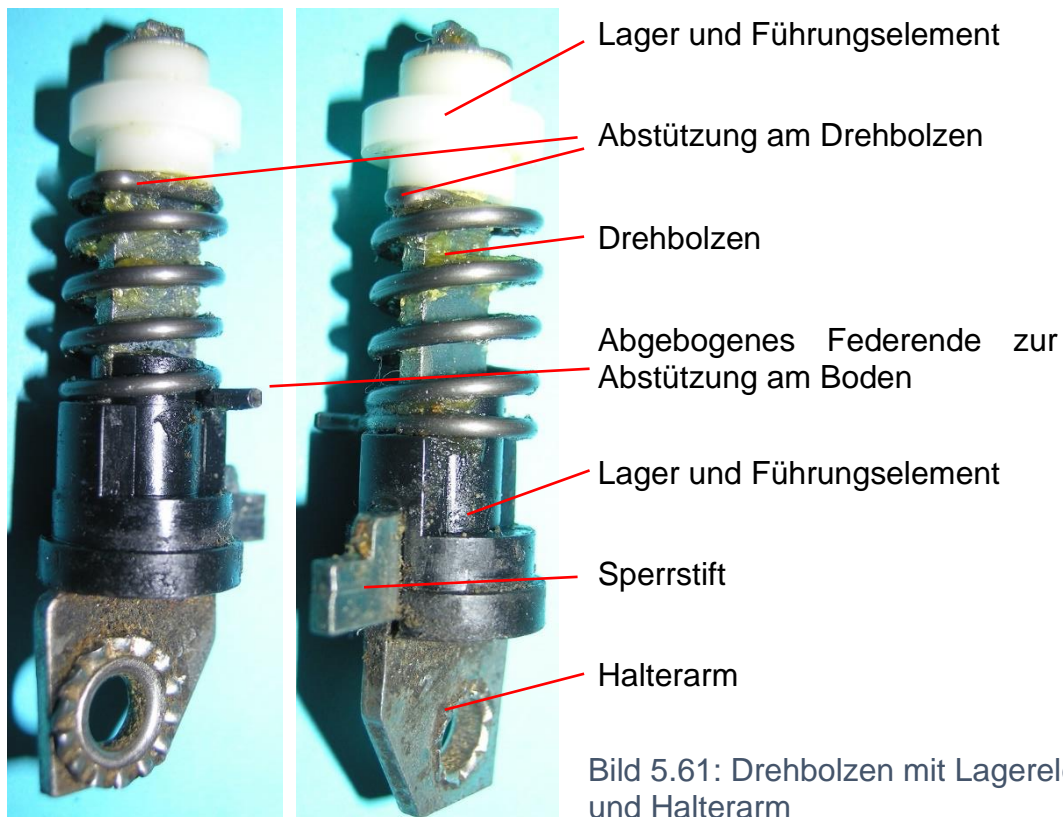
Drehbolzen mit Lagerelementen und Halterarm
